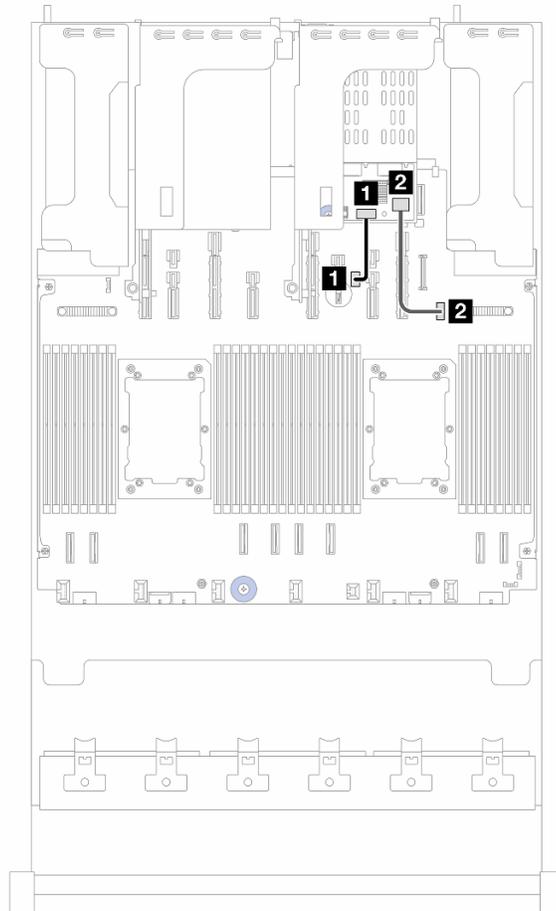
Kabelführung für hintere Rückwandplatine für M.2-Laufwerke
